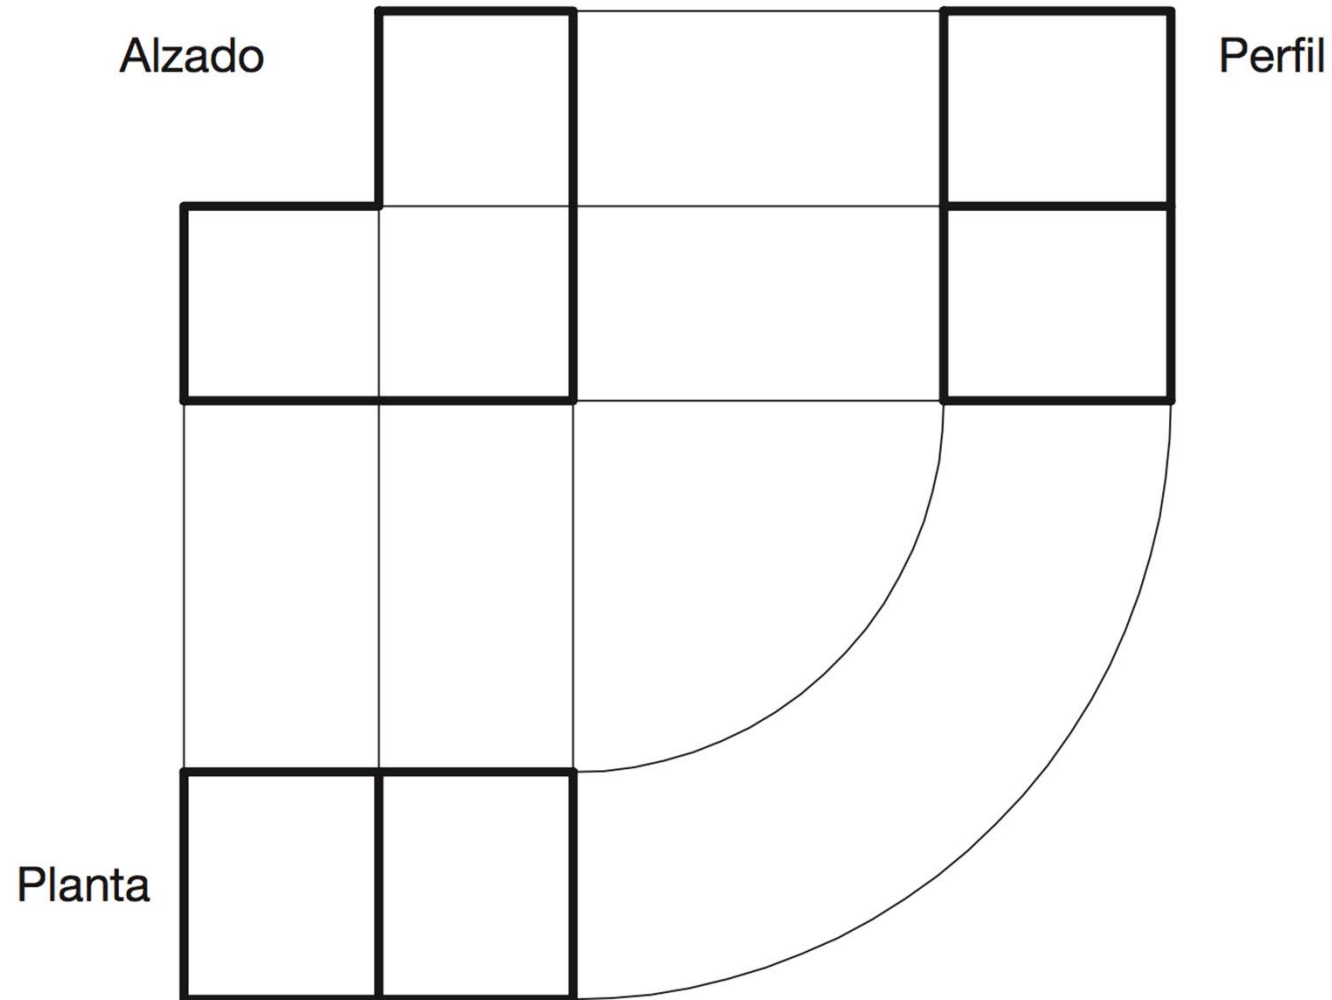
Obtención del perfil de un objeto mediante la planta y el alzado.
